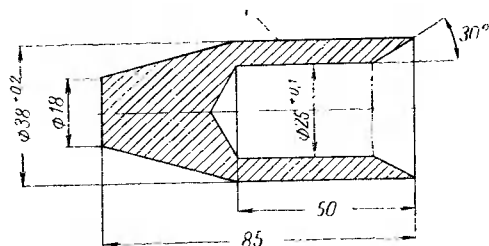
Оправка для установки крышки подшипника ведущего вала
